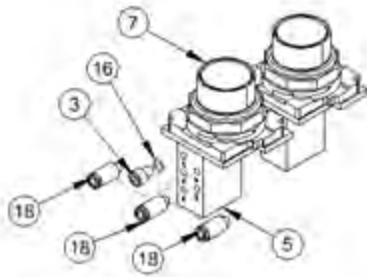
FF3000 Liste des pièces de l'ensemble châssis principal (RÉF. 35686)
